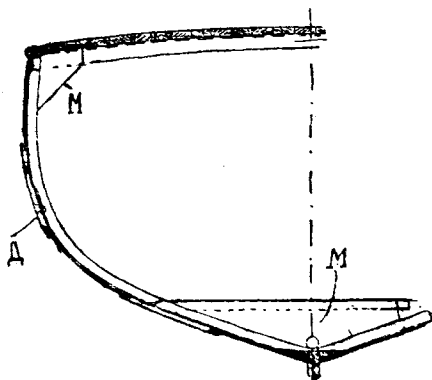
Корпусъ стальной лодки.—М, угольники для пола и поддерживающіе палубу (соединяющіе шпангоуты съ бимсами) для приданія корпусу большей прочности и для уменьшенія дрожанія. Обшивка Д чередуется: листъ прикрѣпленъ къ шпангоутамъ, а слѣдующій листъ приклепанъ краями сверху.
